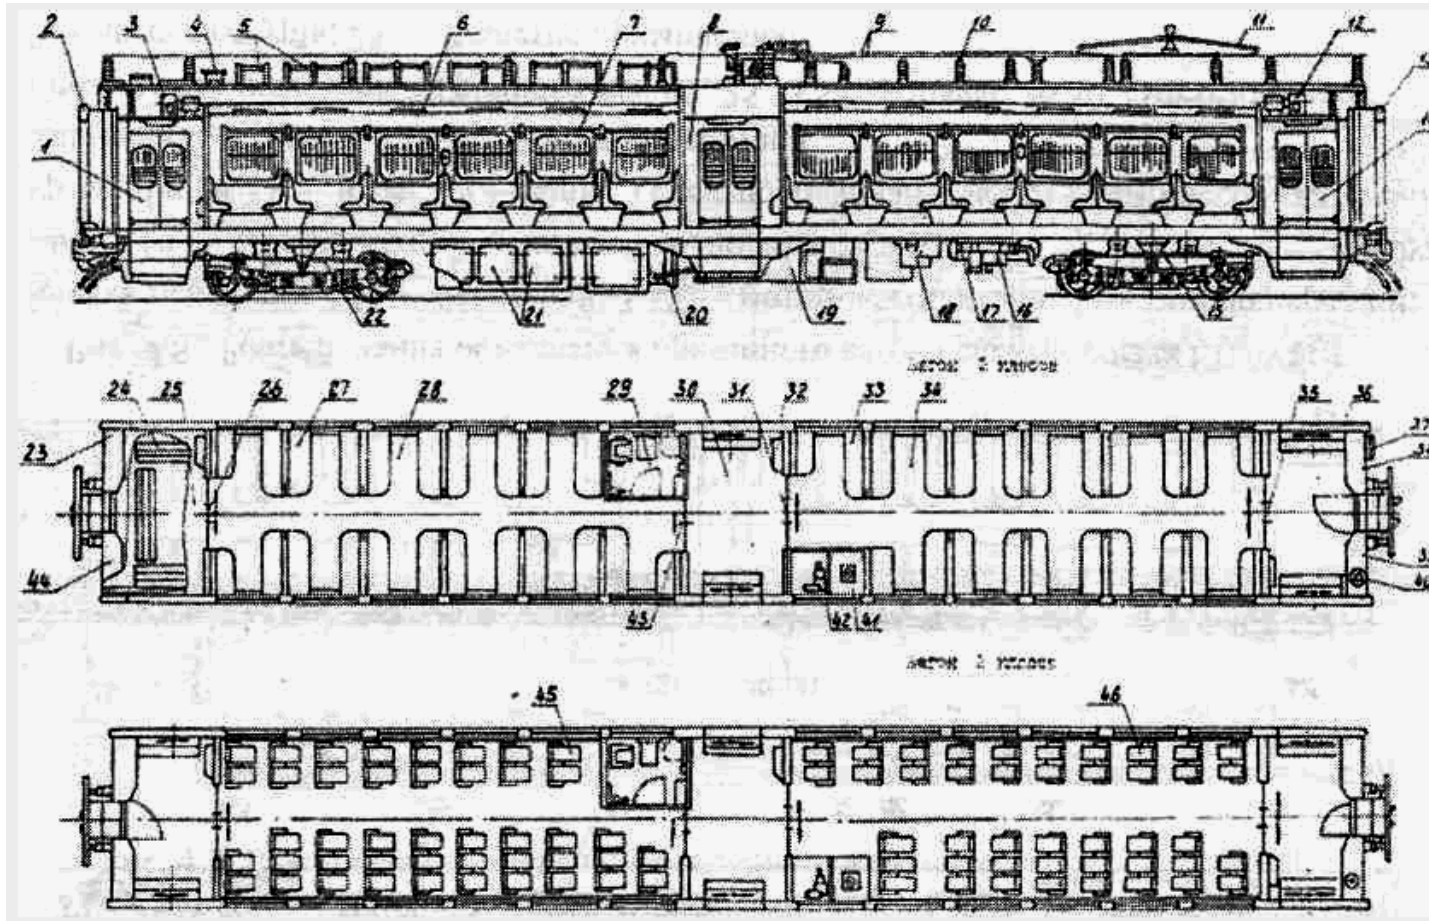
Розташування обладнання моторного вагона ЕПЛ9Т:
